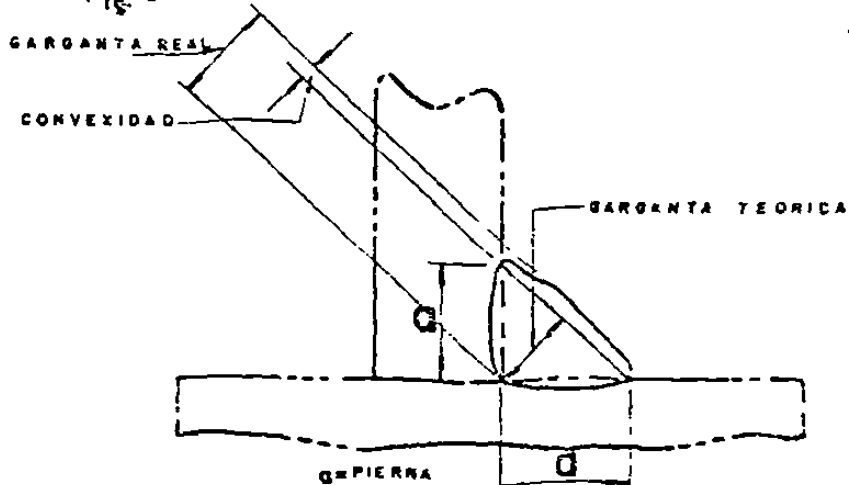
SOLDADURA DE FILETE CONVEXA
